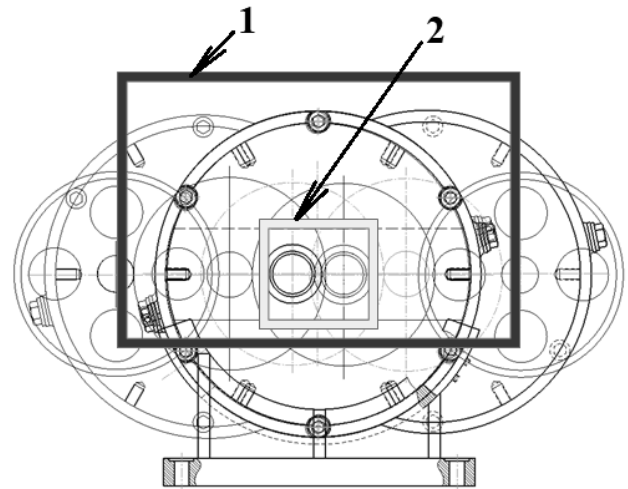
Зона возможного расположения входного вала 1 и выходного вала 2 в вертикальном и горизонтальном направлении при креплении опор к корпусу тихоходной ступени
